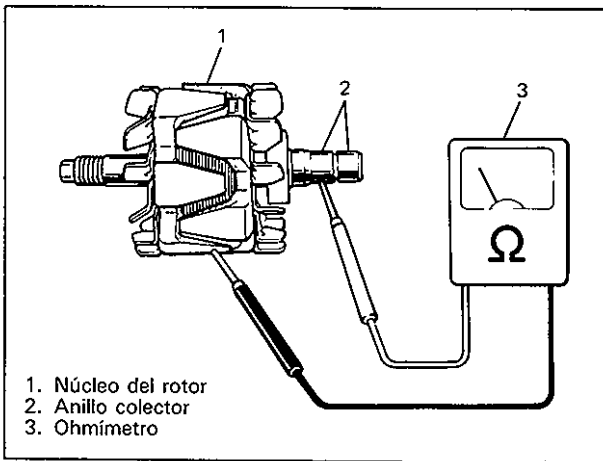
H-17 Comprobación del aislamiento de la bobina de campo
